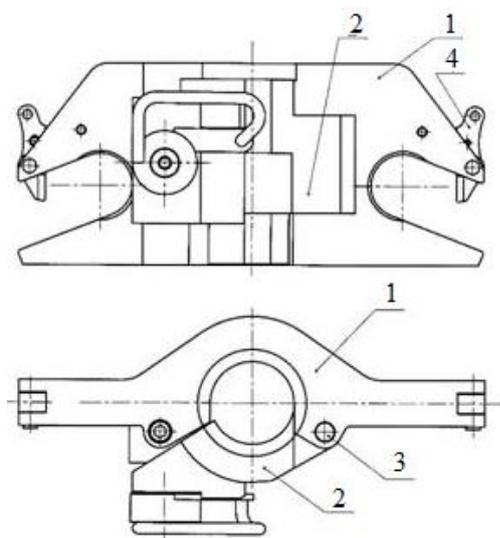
Элеватор трубный ЭХЛ 73-25:
